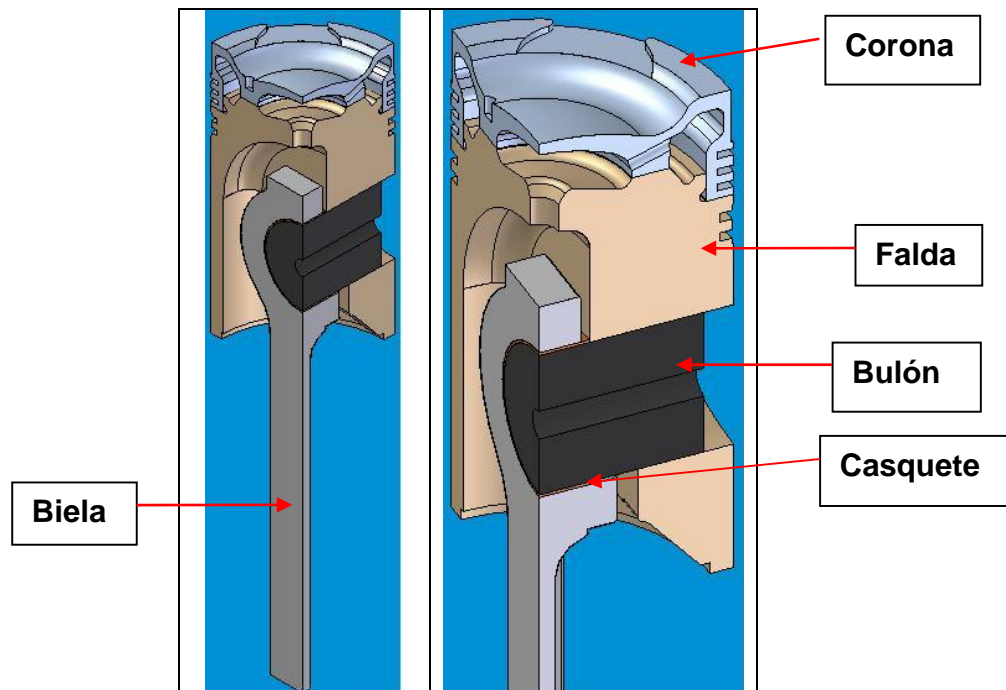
Partes que constituyen el conjunto motriz del motor Allen 8S37G.
